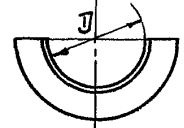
Полуфланец опорный 3ф0-3ф0-26
